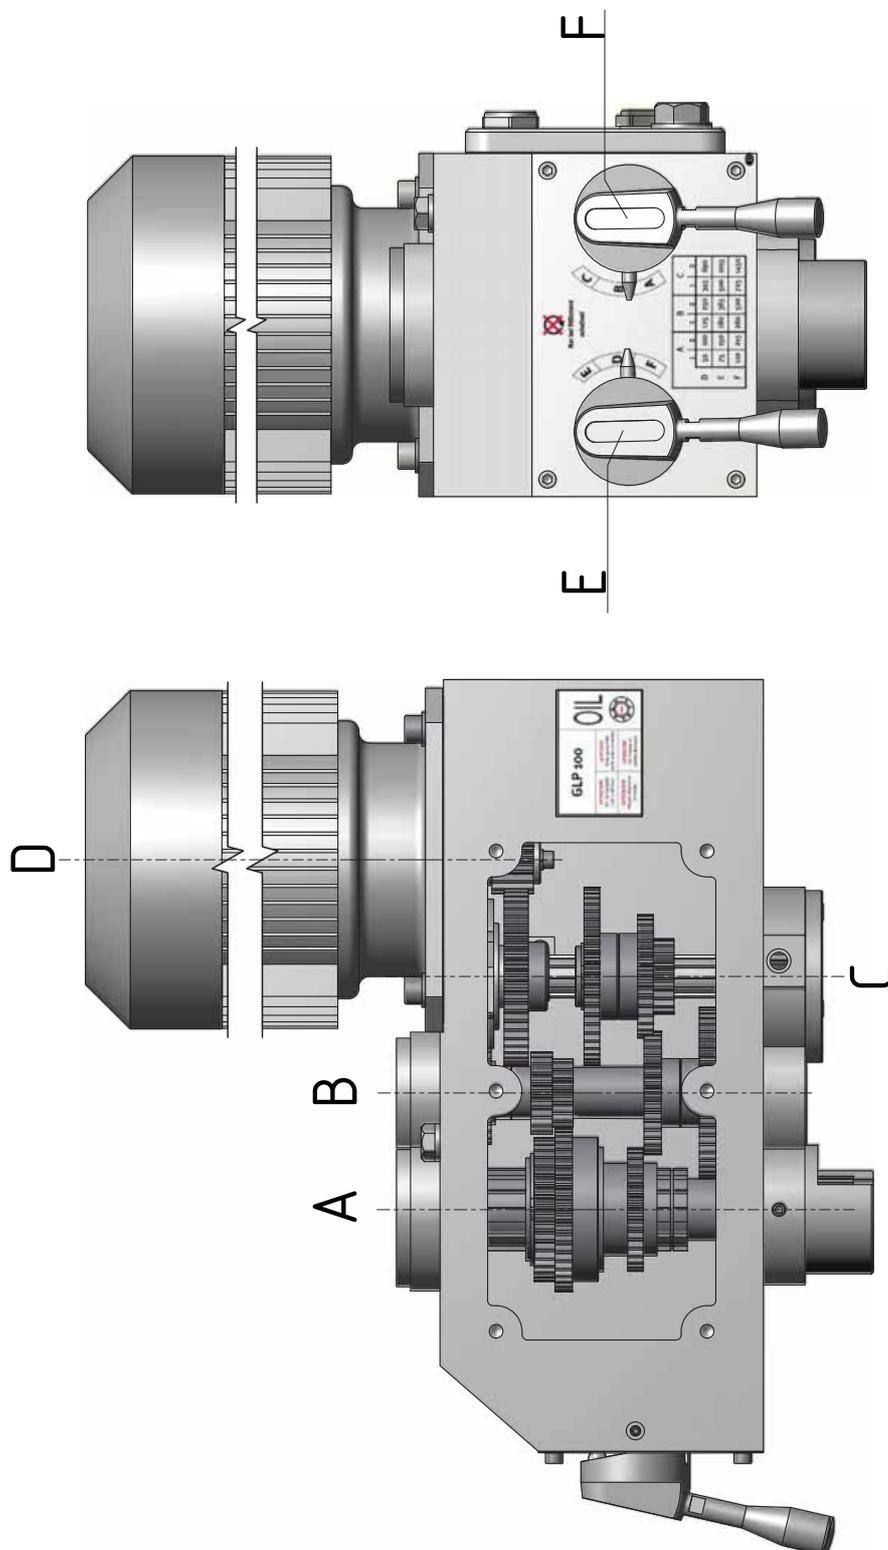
Getriebe Bohrspindel - Gear box main spindle
